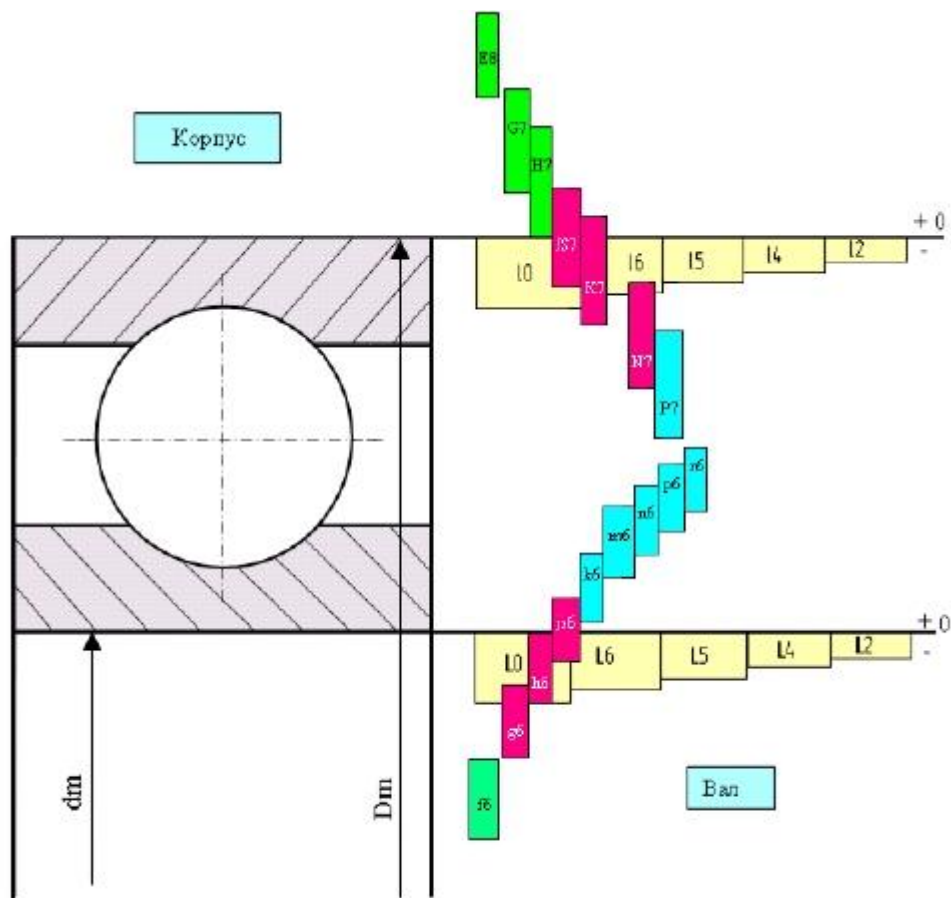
Схема расположения полей допусков для подшипников качения (выборочно)
